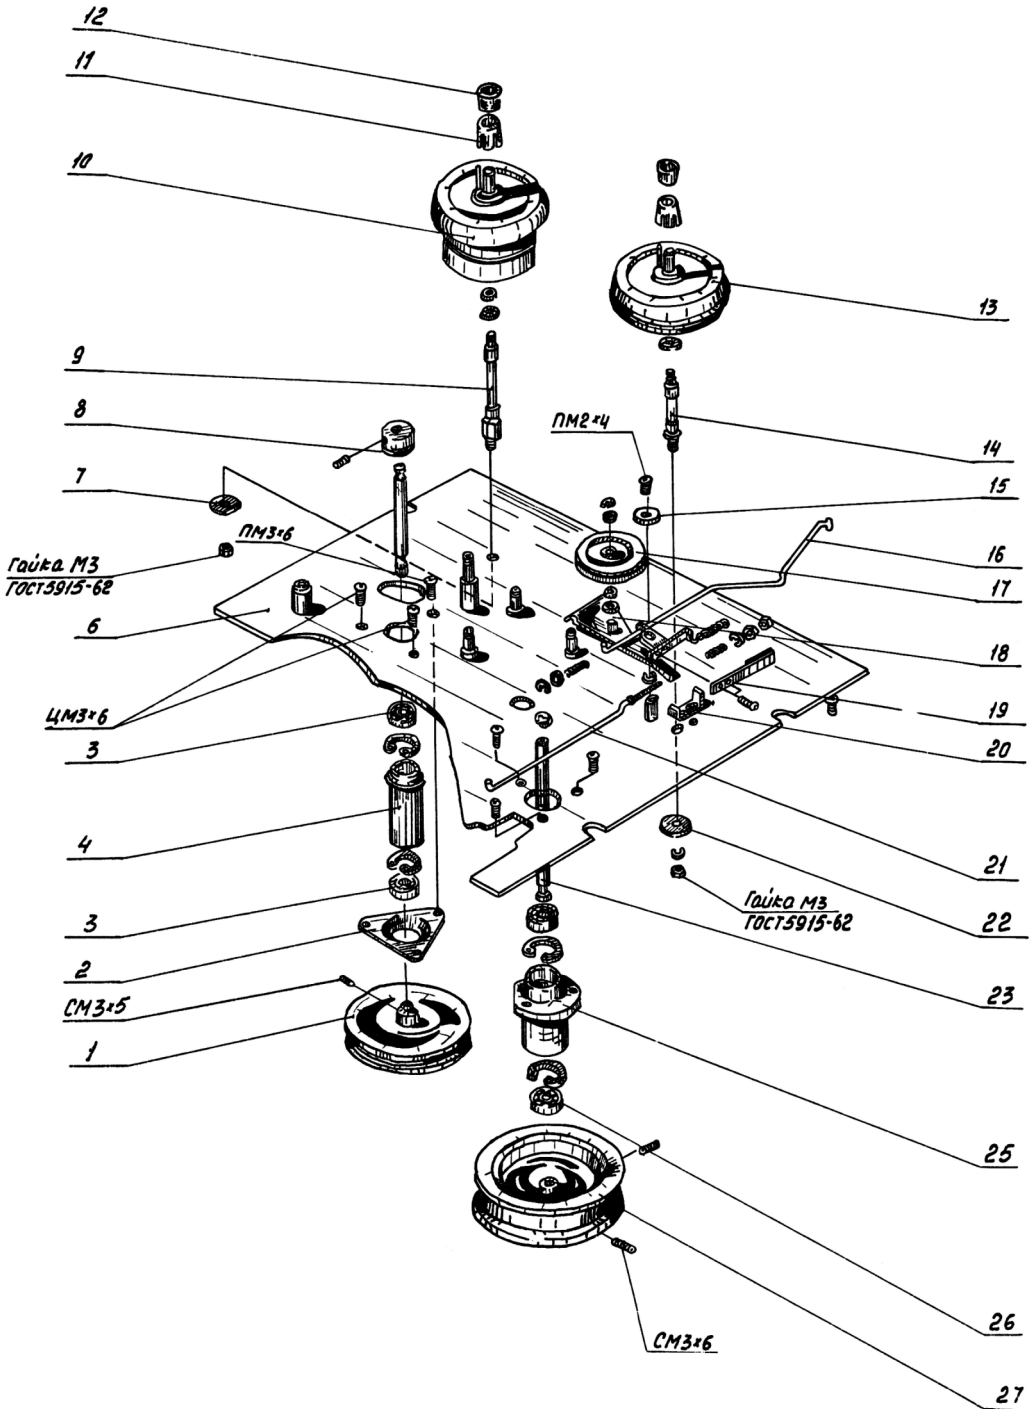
Схема разборки(сборки) ППМ (стадия 1)
